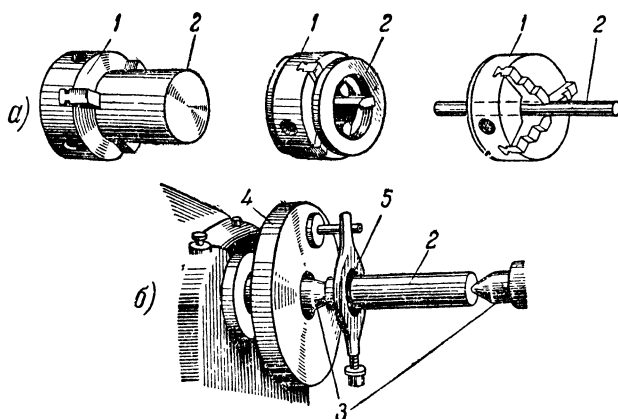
Приспособления для закрепления заготовок на токарном станке.
